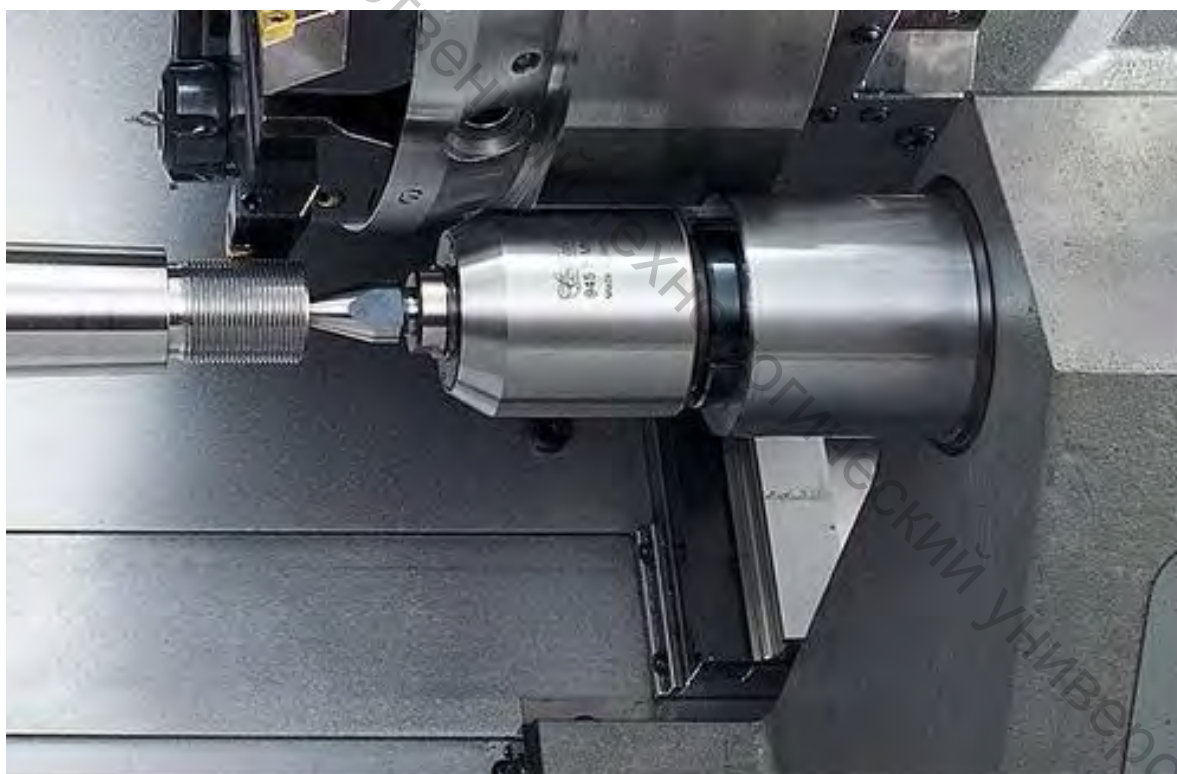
Задняя бабка токарного станка с ЧПУ
